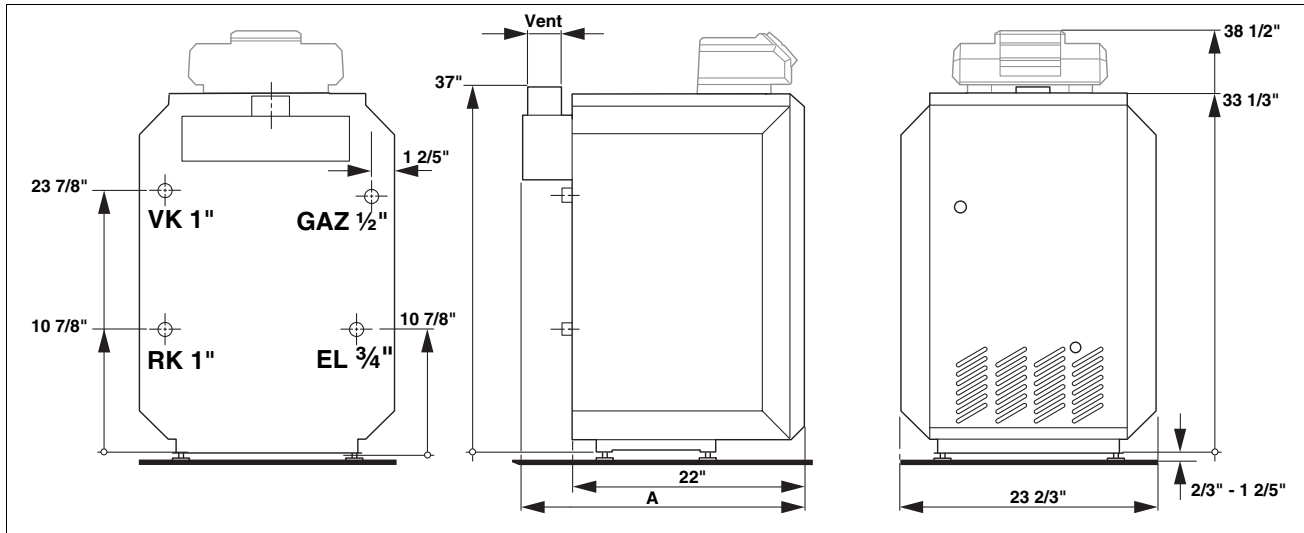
Vues arrière, latérale et avant (dimensions en ")
